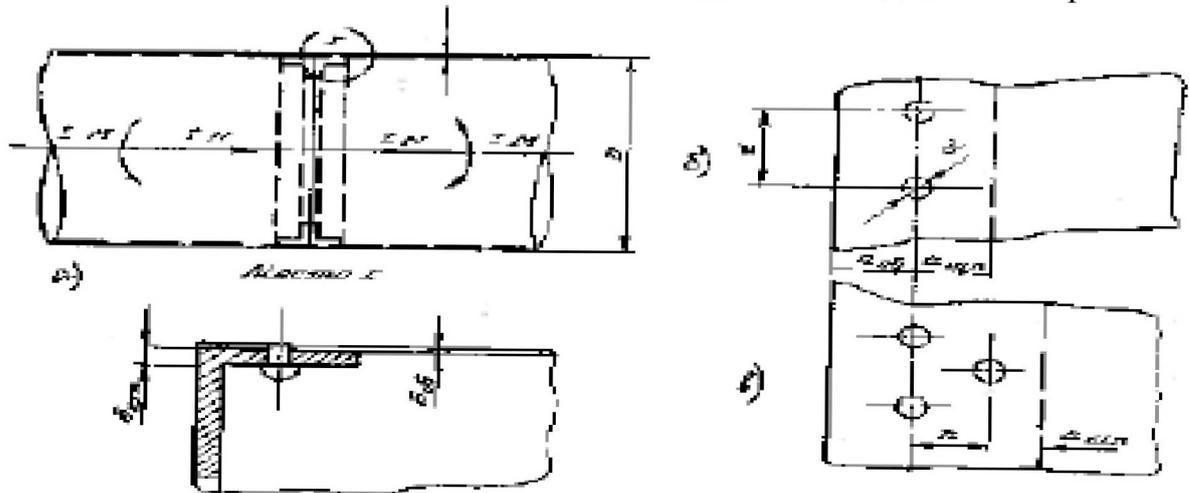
Заклепочное соединение стыкового шпангоута: а – схема нагружения шпангоута, б – однорядный шов, в - двухрядный шов
